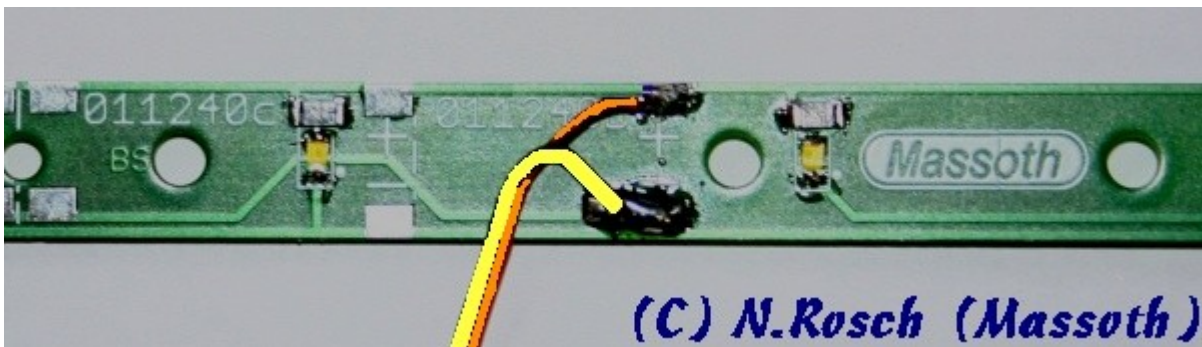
Massoth Lichtleiste mit Kabelanschluss
